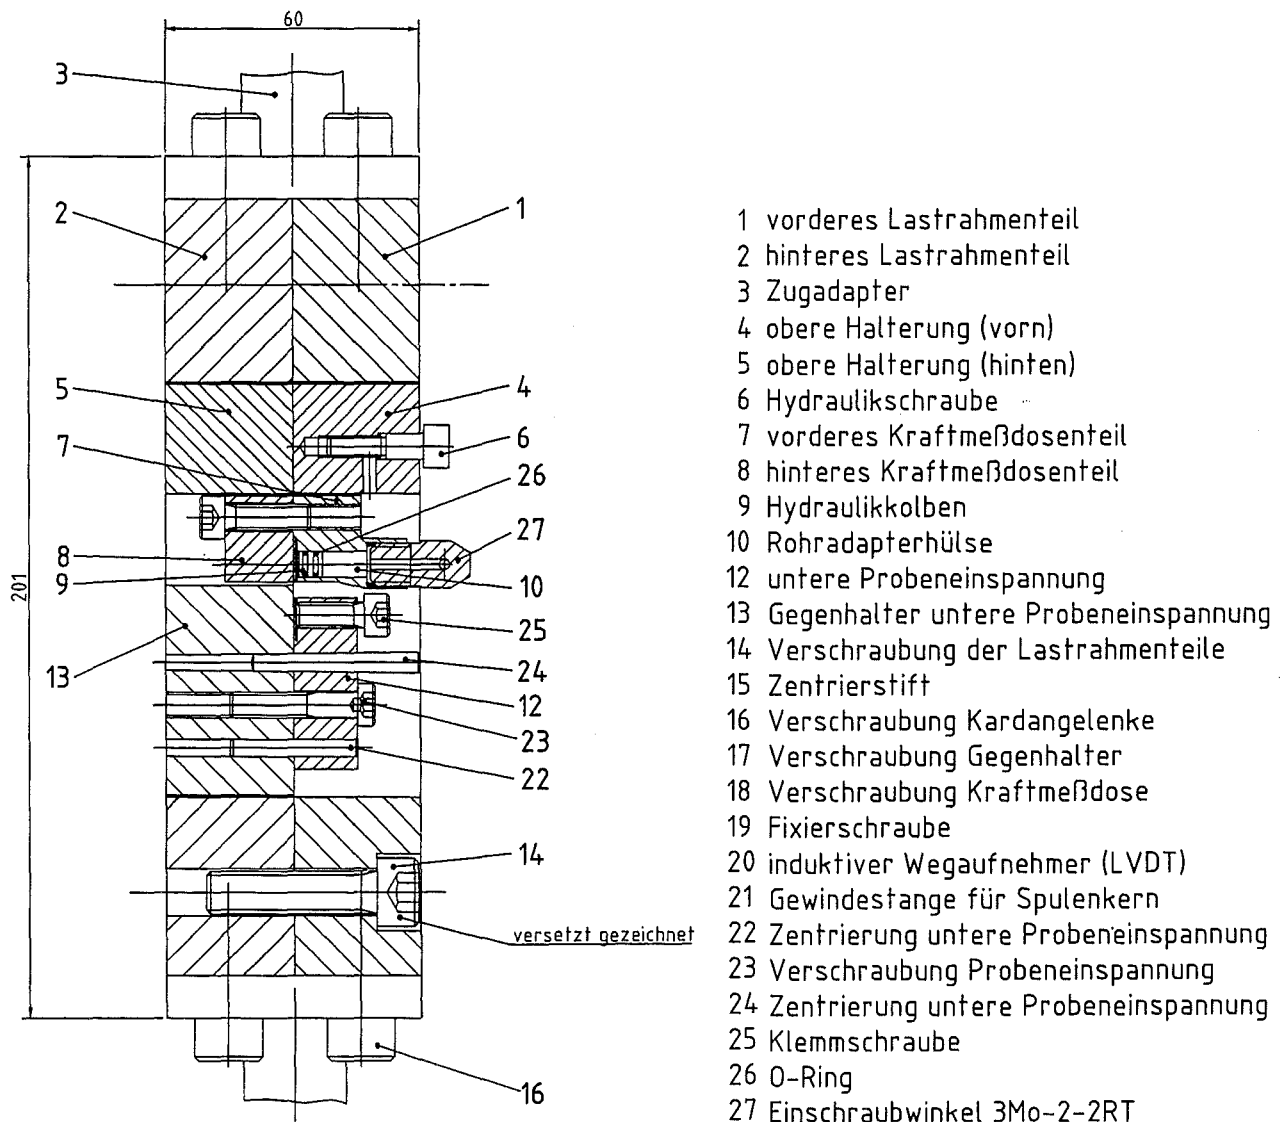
Übersichtszeichnung des Lastrahmens; Seitenansicht A-A (siehe Abb. 3.4) im Mittelschnitt.
